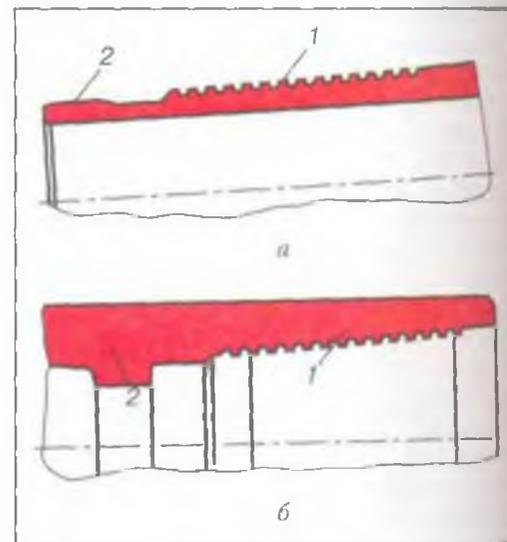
Конструкция резьбовых соединений: а – безмуфтового на трубе; б – на муфте: 1 – резьба «Тrapeция»; 2 – уплотнительная поверхность.
